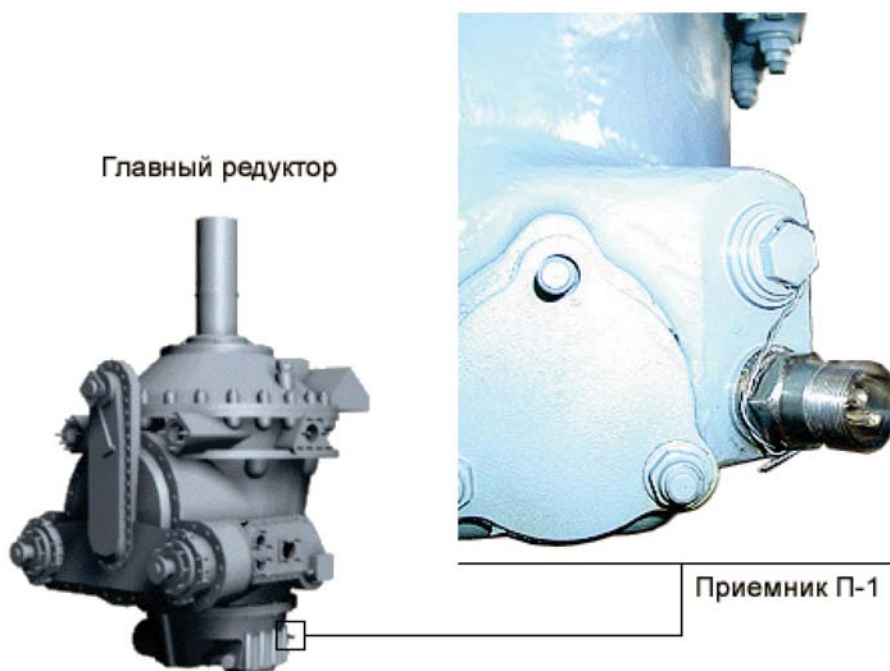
Установка приемника П-1 на главном редукторе для измерения температуры масла главного редуктора
